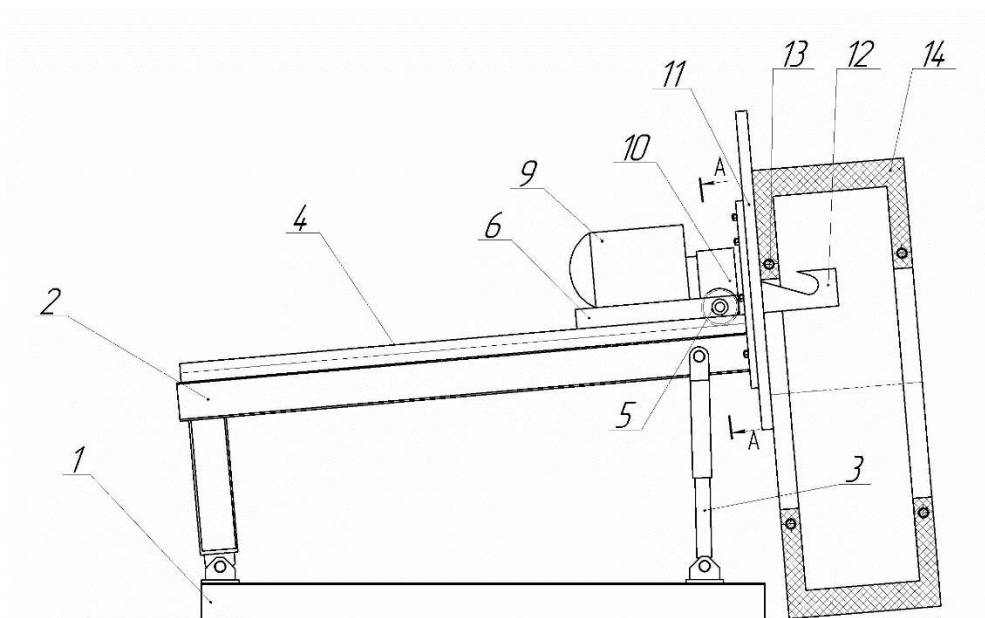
Установка для извлечения бортовых колец из шин с электромеханическим приводом [98]
